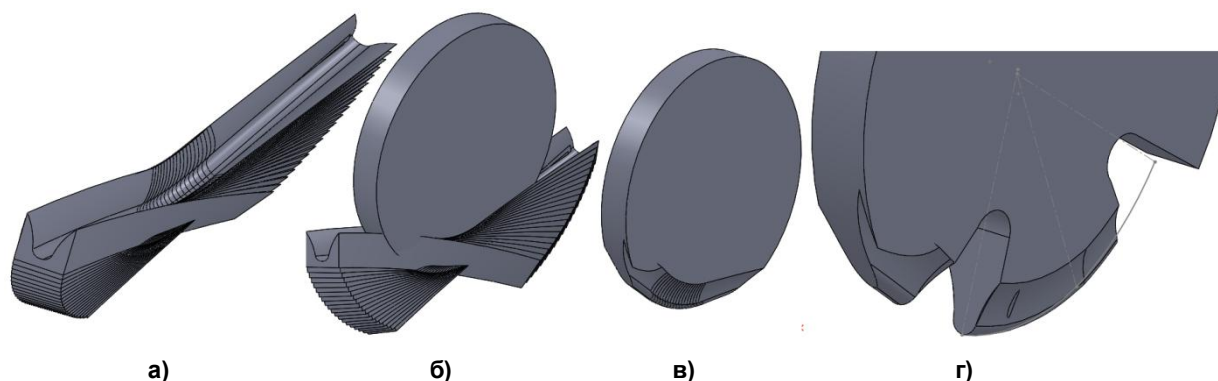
Множество фрагментов в области впадины зуба колеса (а), дисковая «заготовка» фрезы (б), разность этого тела с множеством фрагментов колеса (в), тело «заготовки» фрезы со стружечными канавками (г)
